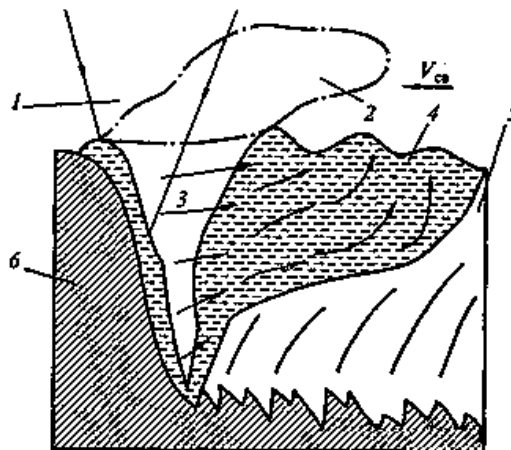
Схема зварювальної ванни при лазерному зварюванні [14]: 1 – лазерний промінь; 2 – плазмовий факел; 3 – парогазовий канал; 4 – хвостова частина ванни; 5 – метал шва; 6 – метал, що зварюють; $V_{зв}$ – напрям зварювання.
